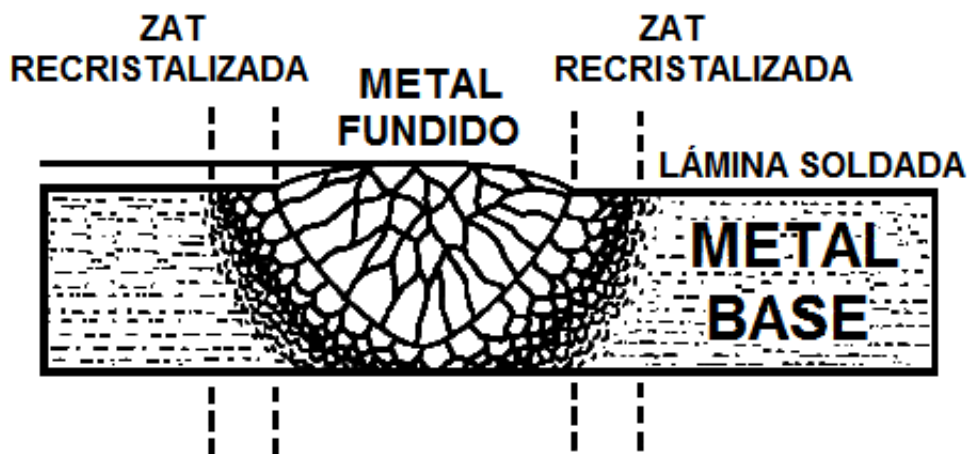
Esquema de las zonas involucradas en un cordón de soldadura (8, 18)
